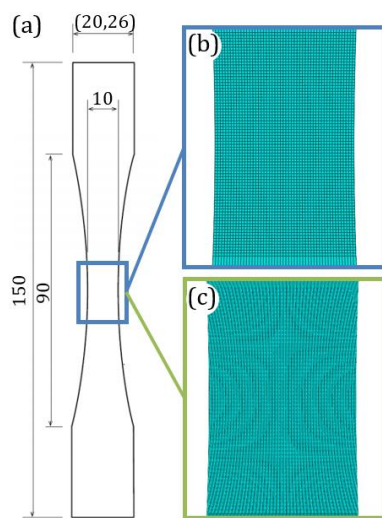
22: Maillage des éprouvettes de traction plate, (a) dimension de l'éprouvette, (b) éprouvette 6082-T4, taille de maille = 0,2 mm, (c) éprouvette 6082-T6, taille de maille = 0,05 mm
